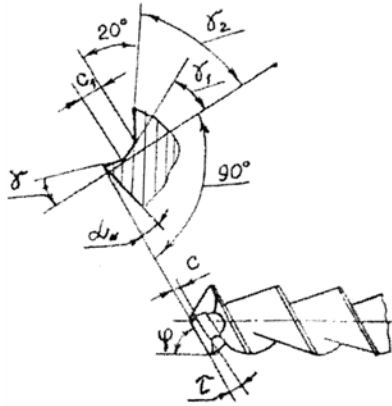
Форма передней поверхности шнекового сверла
